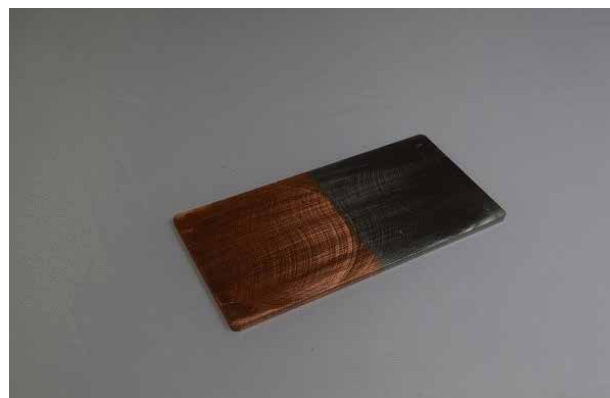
Пример детали, полученной лазерной сваркой двух разных тонколистовых металлов
